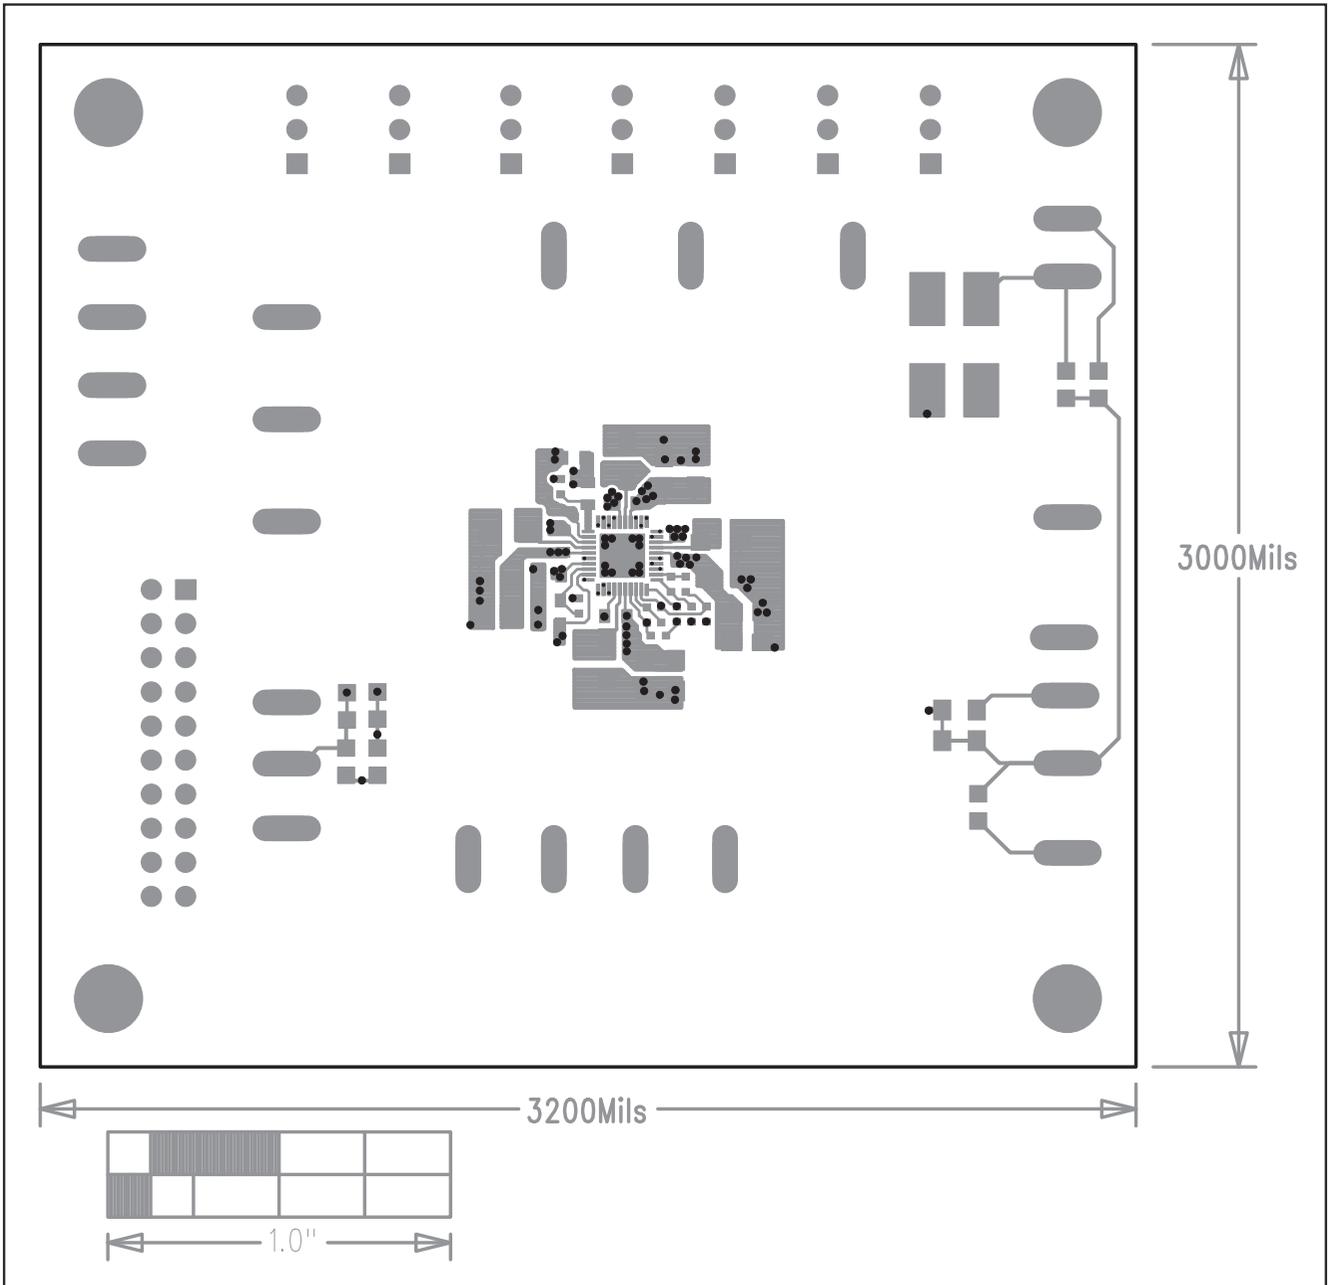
MAX8660 评估板 PCB 布局—元件层第 1 层
